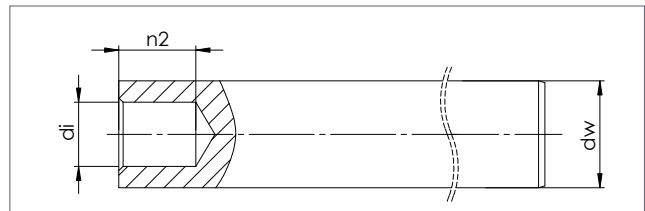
Zusammengesetzte Wellen / Compound shafts
